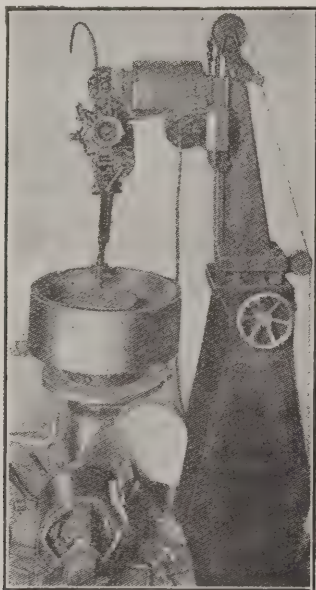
Assemblage par soudure de pièces de frein.
